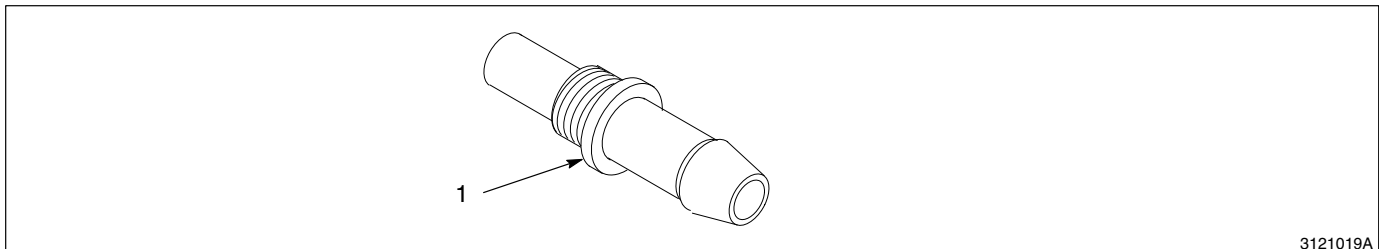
Adattatore del tubo con diam. int. da 9.525 mm per adattatori di spurgo
